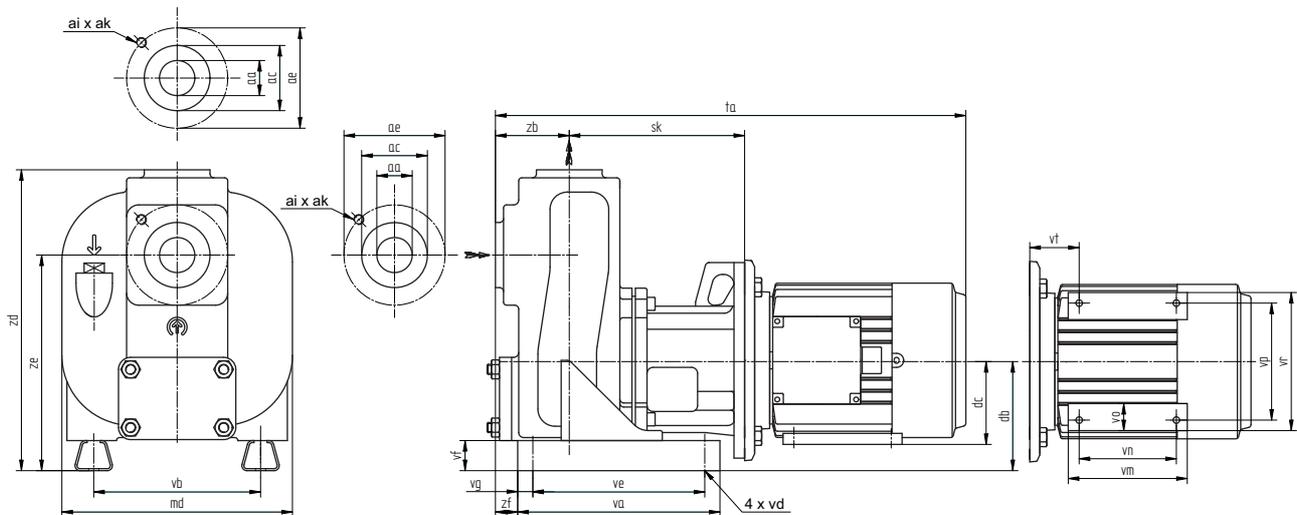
FRES mit ISO 7005 PN20 Anschlüssen.
